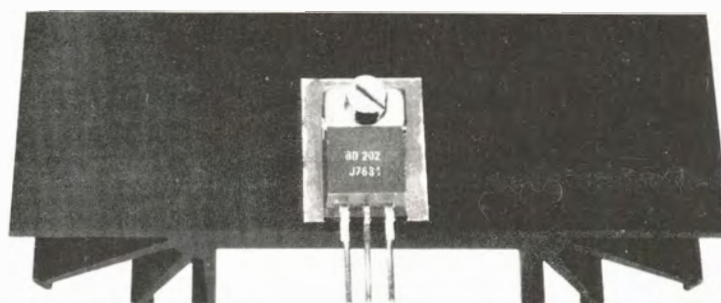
Montaje con tornillo aislado del encapsulado TO-220.
